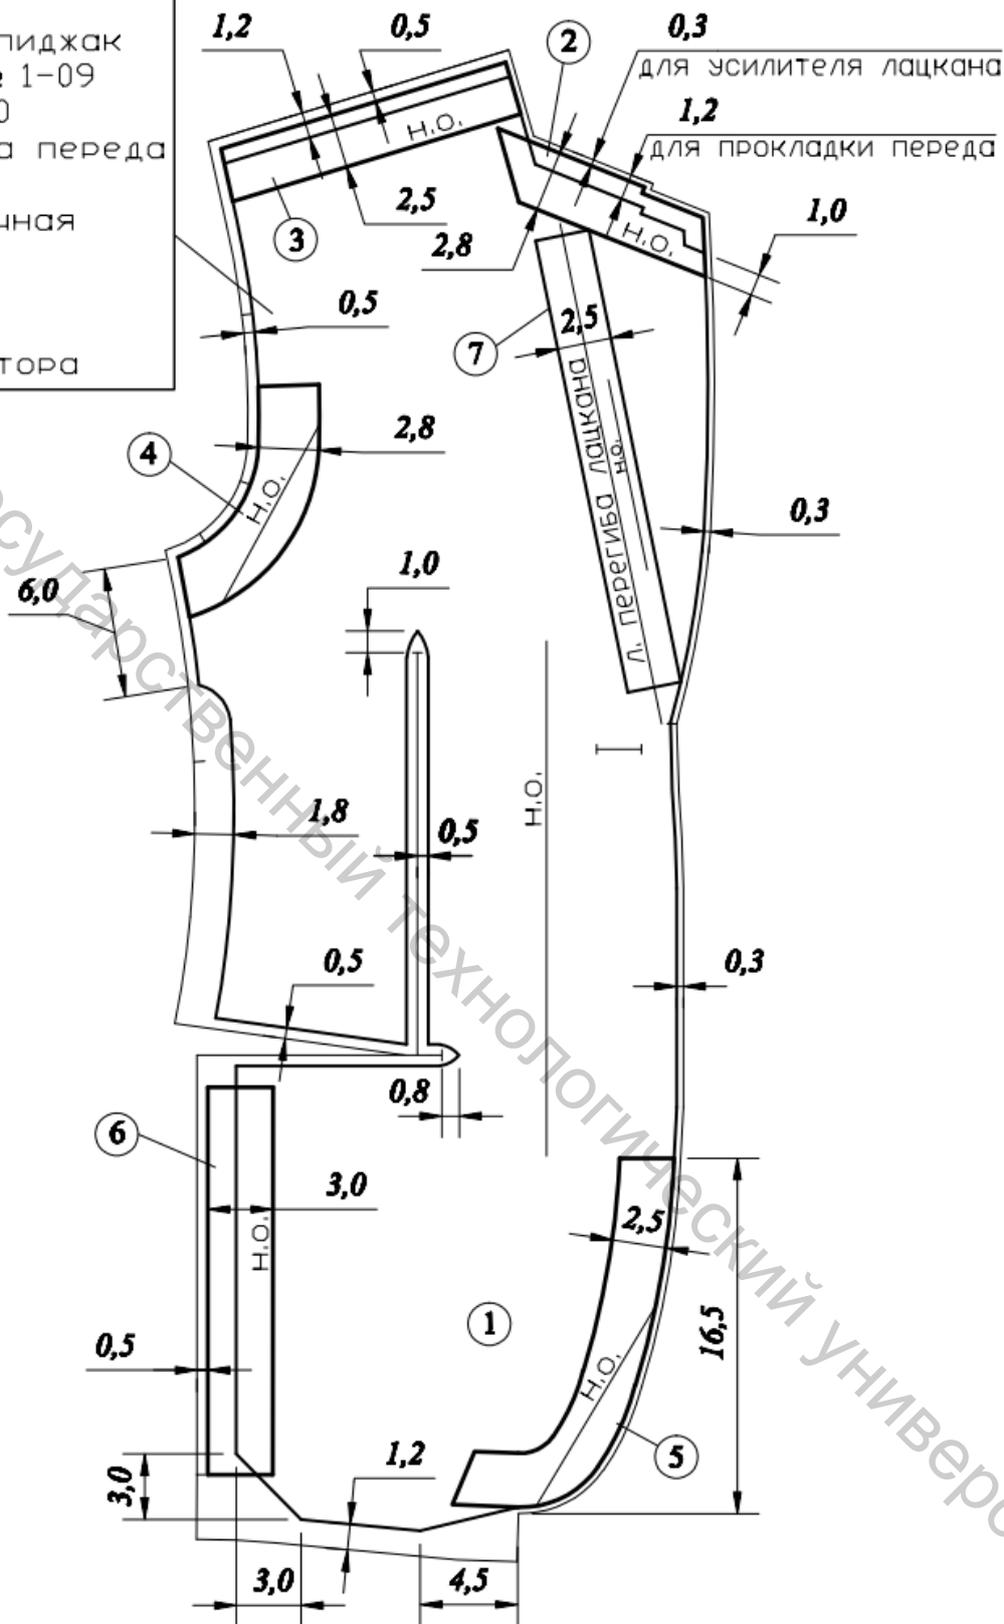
Схема построения чертежей лекал деталей прокладок переда
